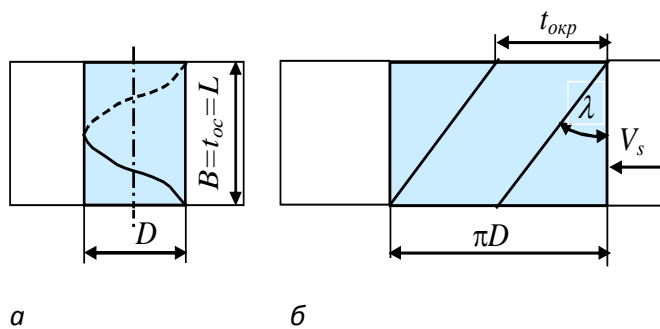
Резание фрезой с винтовой режущей кромкой: а – фрезерование;
